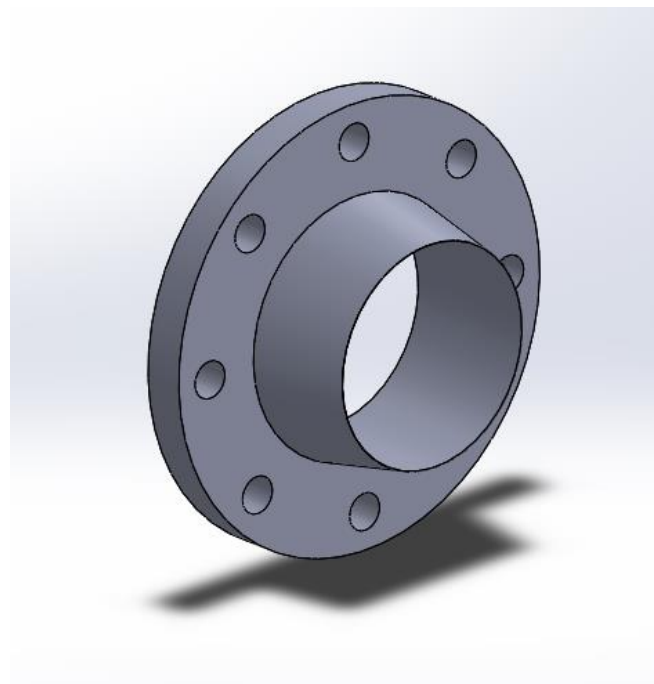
Modelado Brida Welding Neck Class 150 lbs DN100
